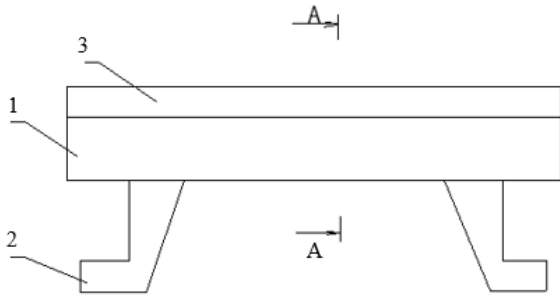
Загальний вигляд колосника з посиленою основою (вигляд збоку): 1 – верхній опорний рожок; 2 – нижній опорний рожок (елементи замкового кріплення); 3 – основне робоче тіло
